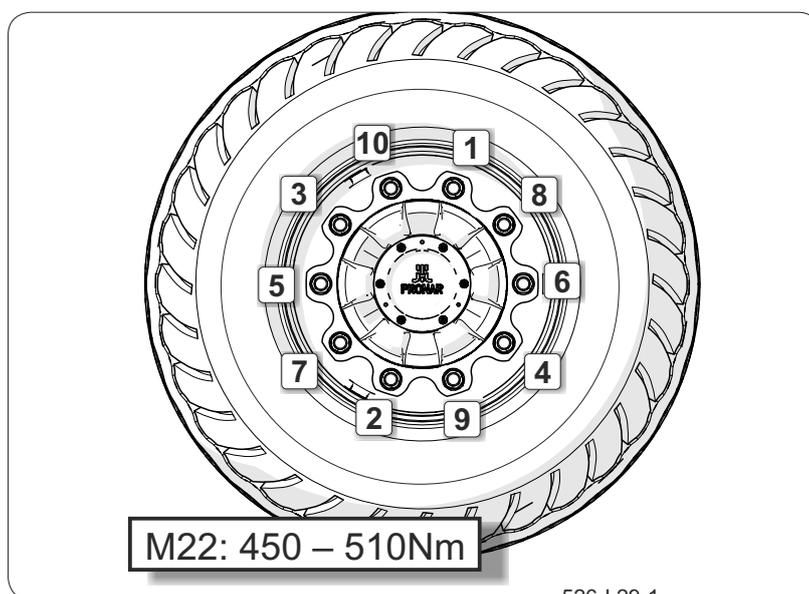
Ordre de serrage des écrous (10 pièces)
